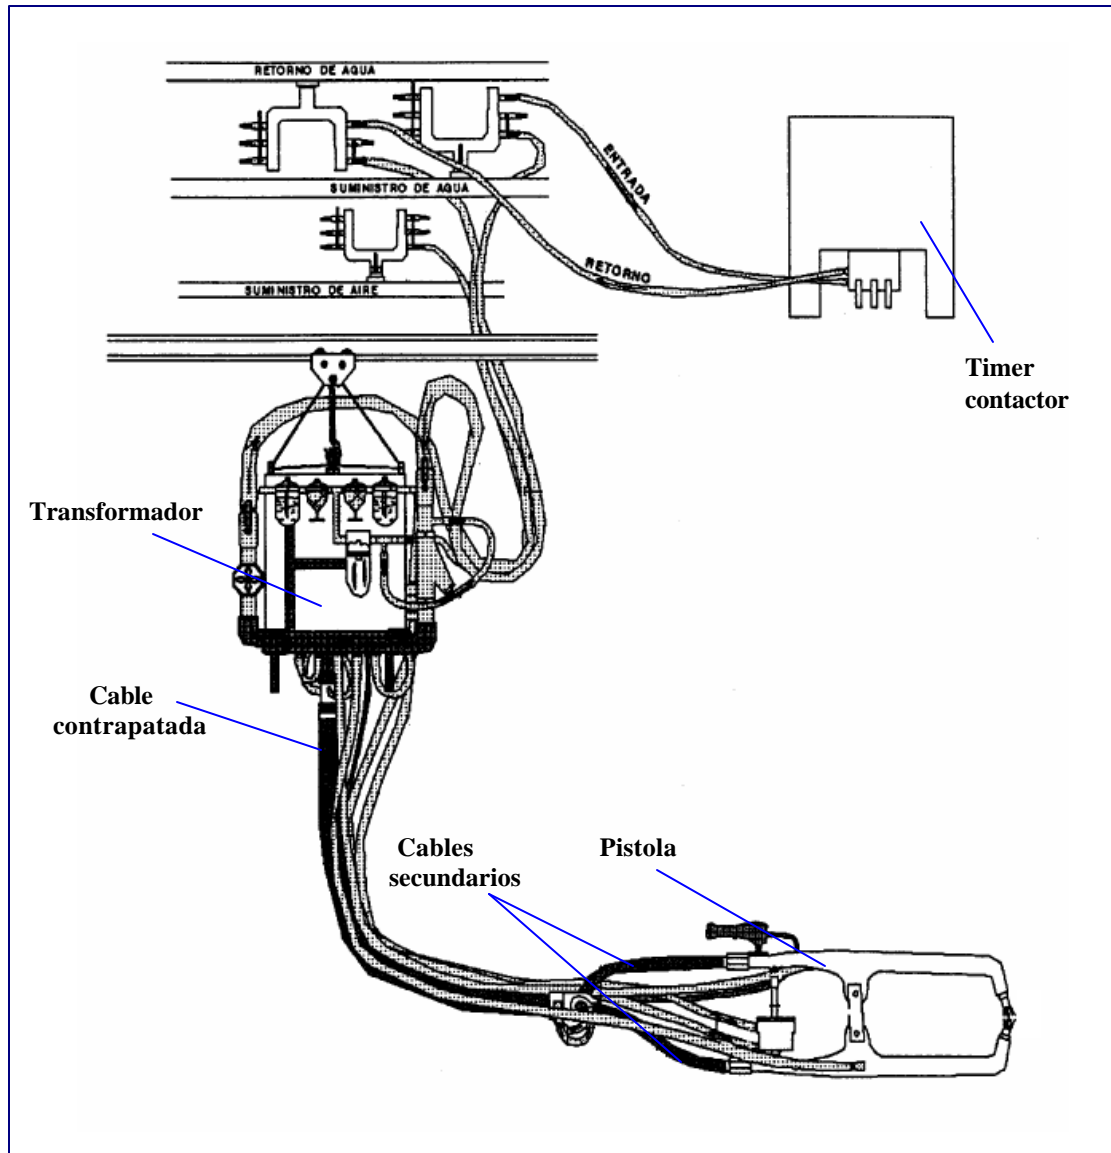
Equipo de soldadura por electropunto con una pistola
